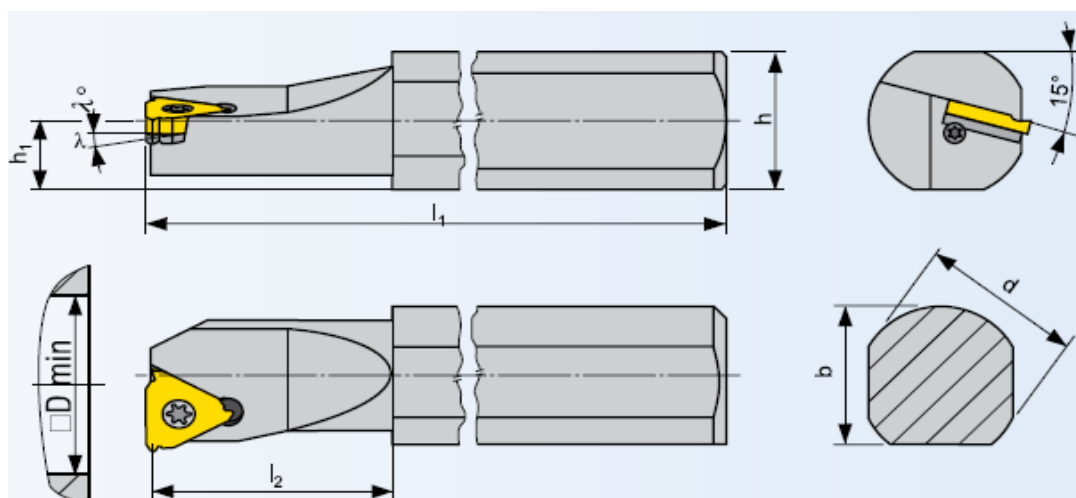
Токарный резец для нарезания резьбы в отверстиях
